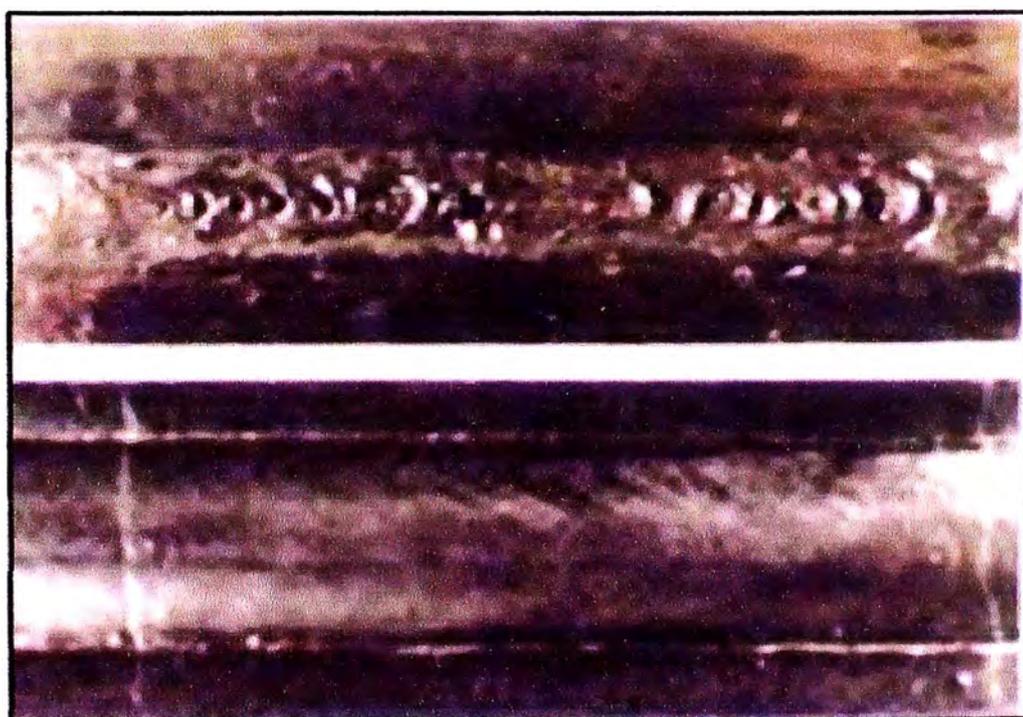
Fisuras longitudinales y transversales en soldaduras con bisel y de filete
